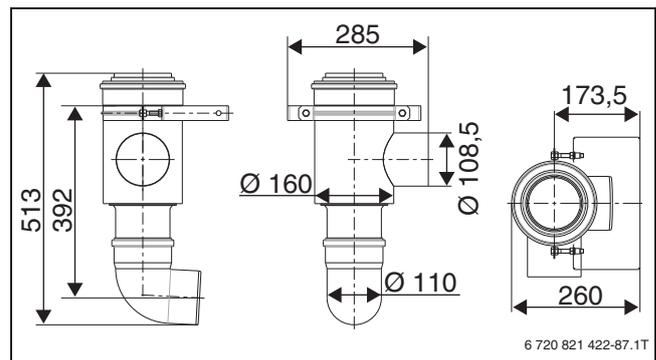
Konzentrisches Kesselanschlussstück für GC7000F 75 ... 300, 75 kW und 100 kW
